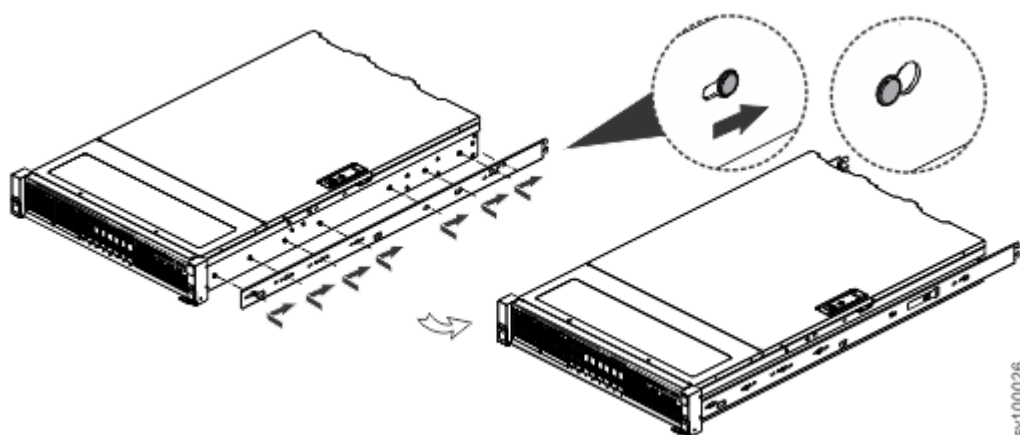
Inneren Teil der Schiene am Chassis befestigen
